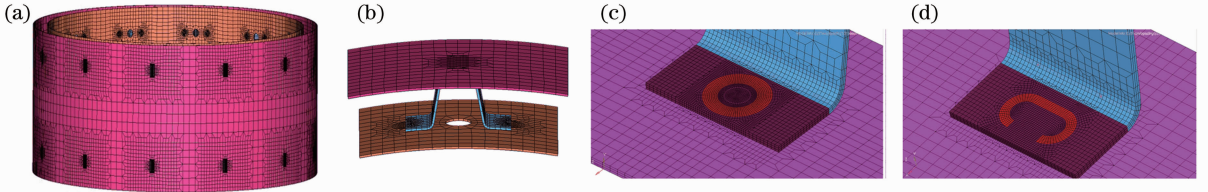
组合构件网格划分。(a) 圆筒件整体; (b) 圆筒件局部; (c) 环形焊缝; (d) C 形焊缝
